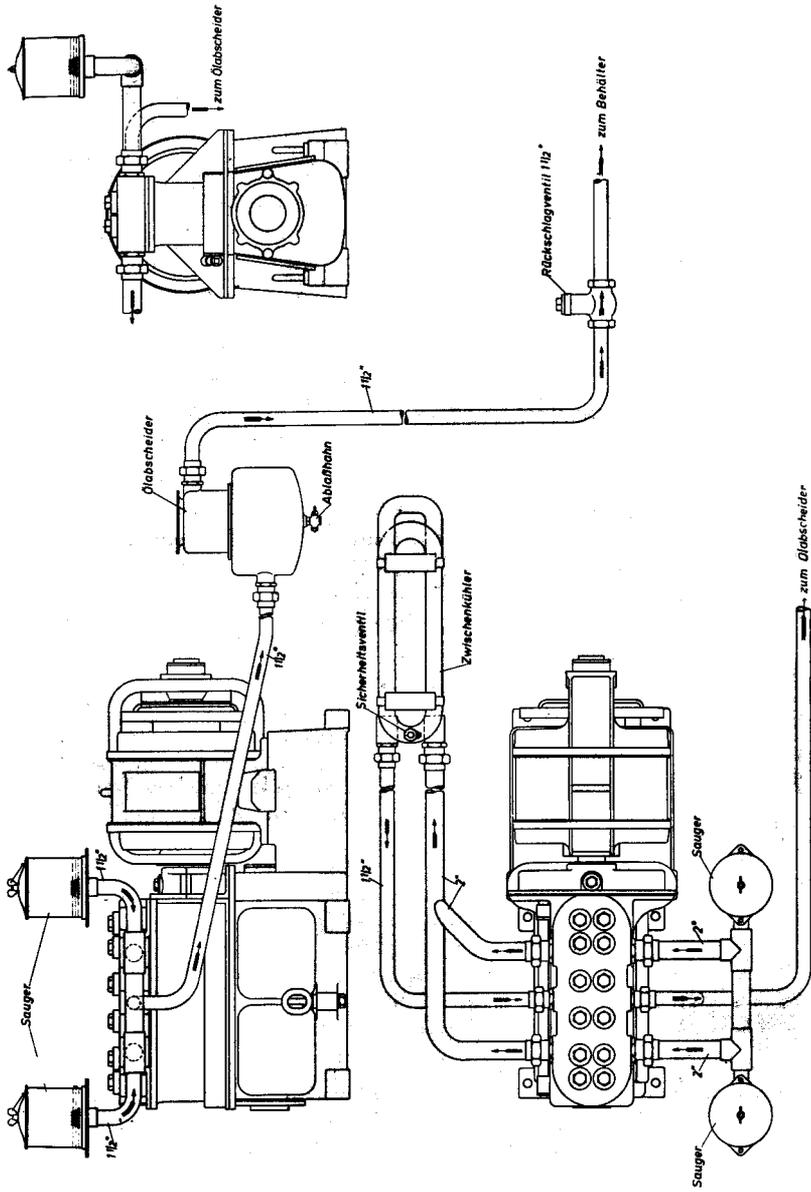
Schaltplan der Motorluftpumpe VW 224
